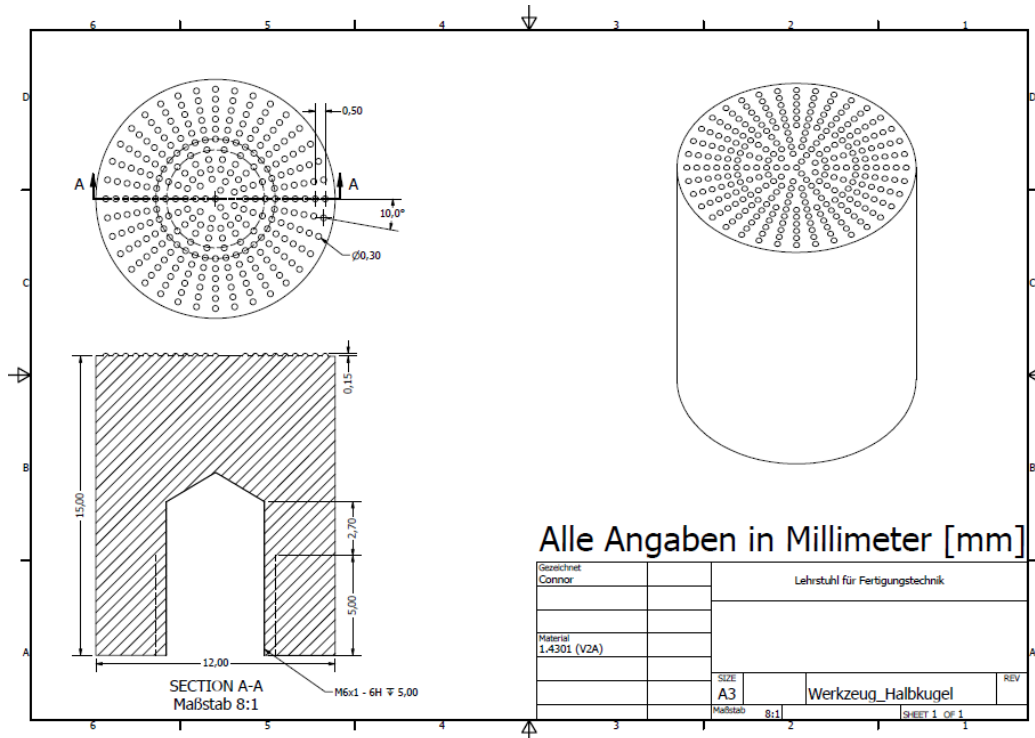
Technische Zeichnung des halbkugelstrukturierten Werkzeugs
